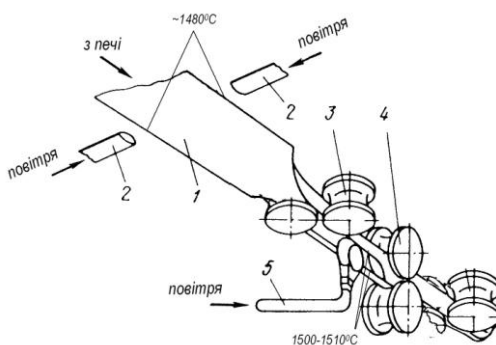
Схема агрегату пічного зварювання 1/2-2"
